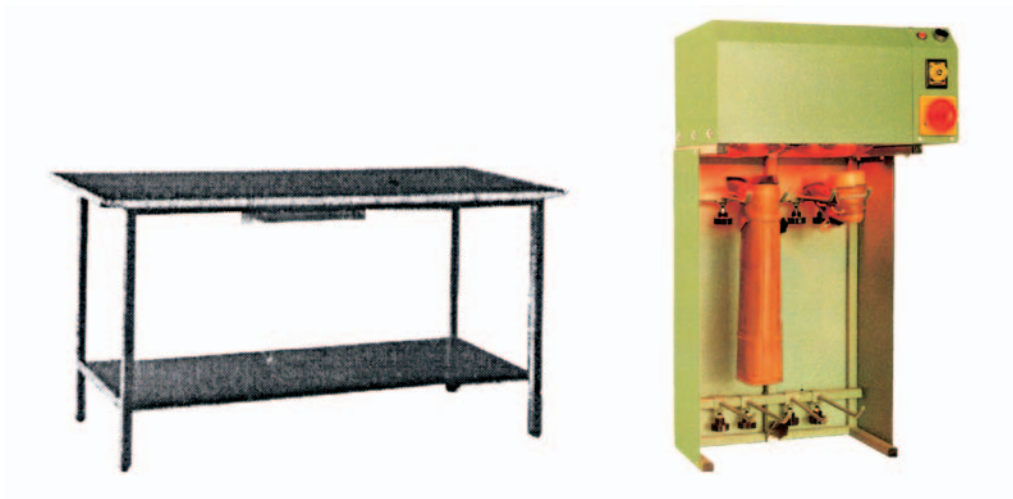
Exemple de table de travail pour collage du fond de la chaussure montée sur la semelle et fourneau pour la réactivation de la colle.
